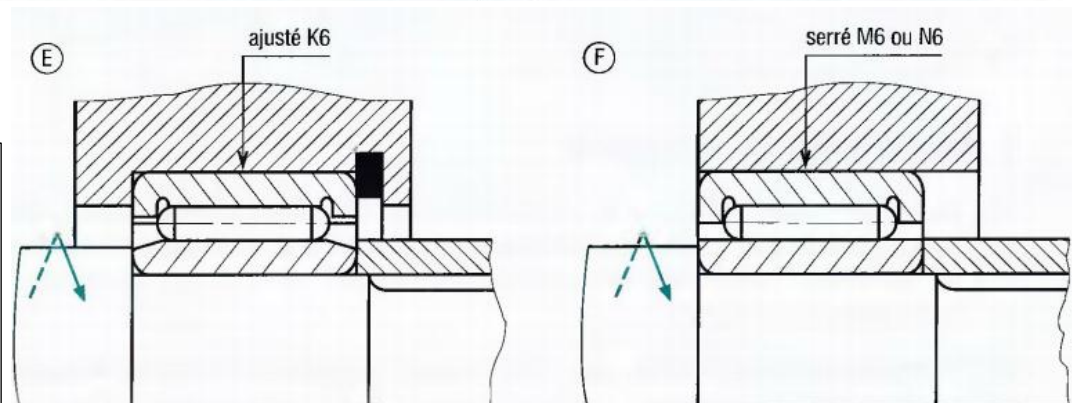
Exemple d'application du principe de montage de roulement à aiguilles.
